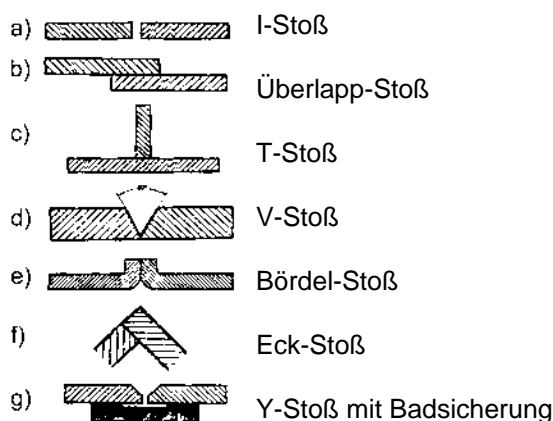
Die wichtigsten Fugenformen beim WIG-Schweißen
